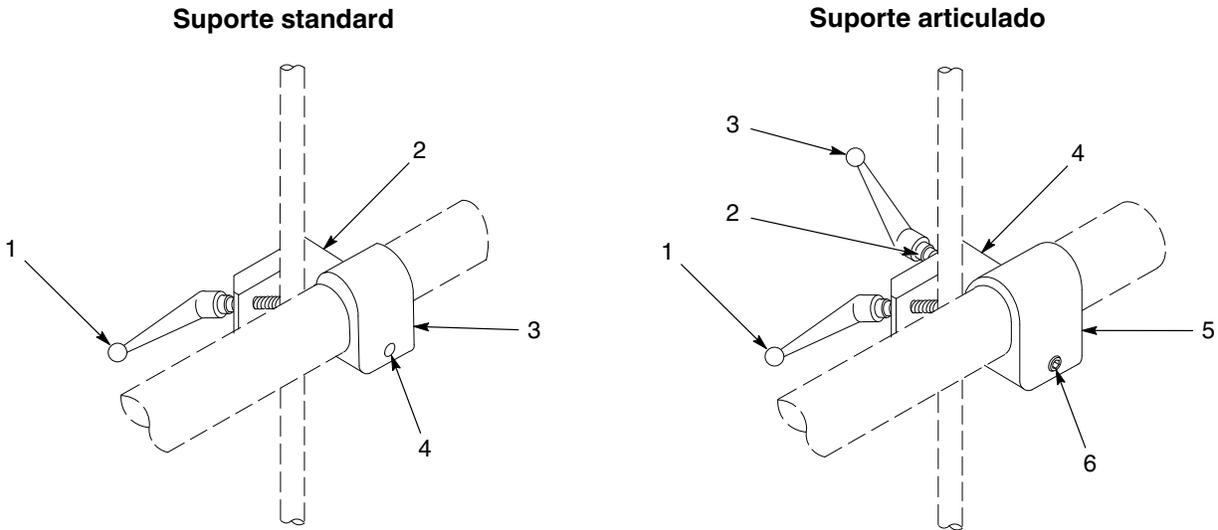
Suportes de barra de pistola para pistolas com tubo de suporte
